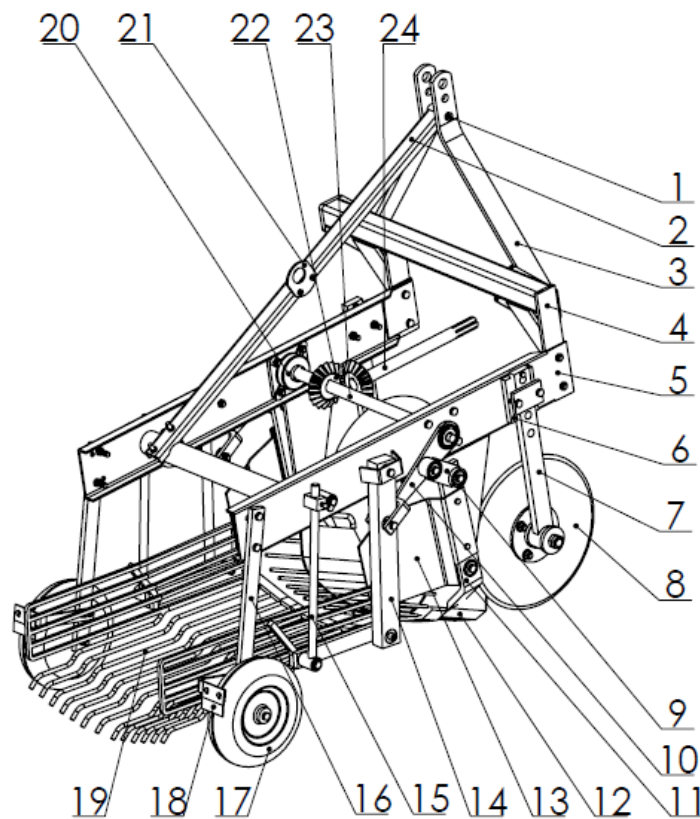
Vue en perspective de la machine en illustrant ses différents composants
